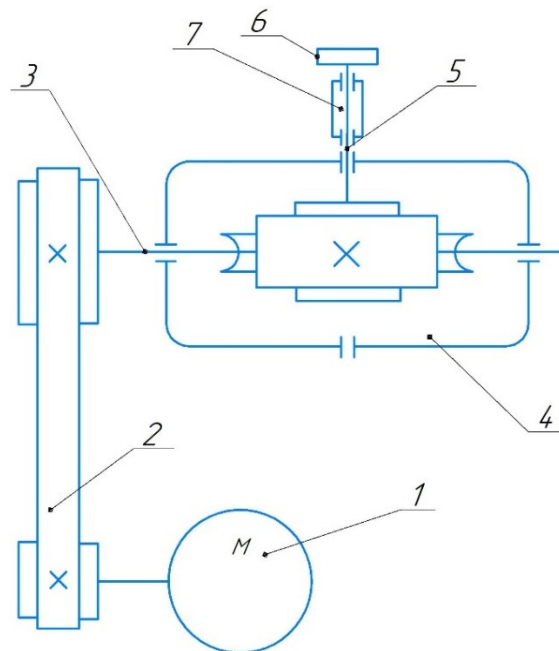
Кінематична схема станку: 1 – електродвигун; 2 – клинопасова передача; 4 – редуктор черв'ячний; 3 – вхідний вал редуктора; 5 – вихідний вал редуктора; 6 – шпиндель; 7 – проміжна опора.
